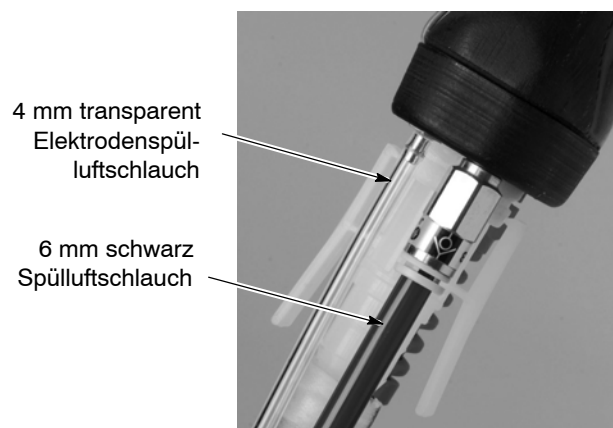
Elektrodenspülluft- und Spülluftschlauch an die Sprühpistole anschließen
